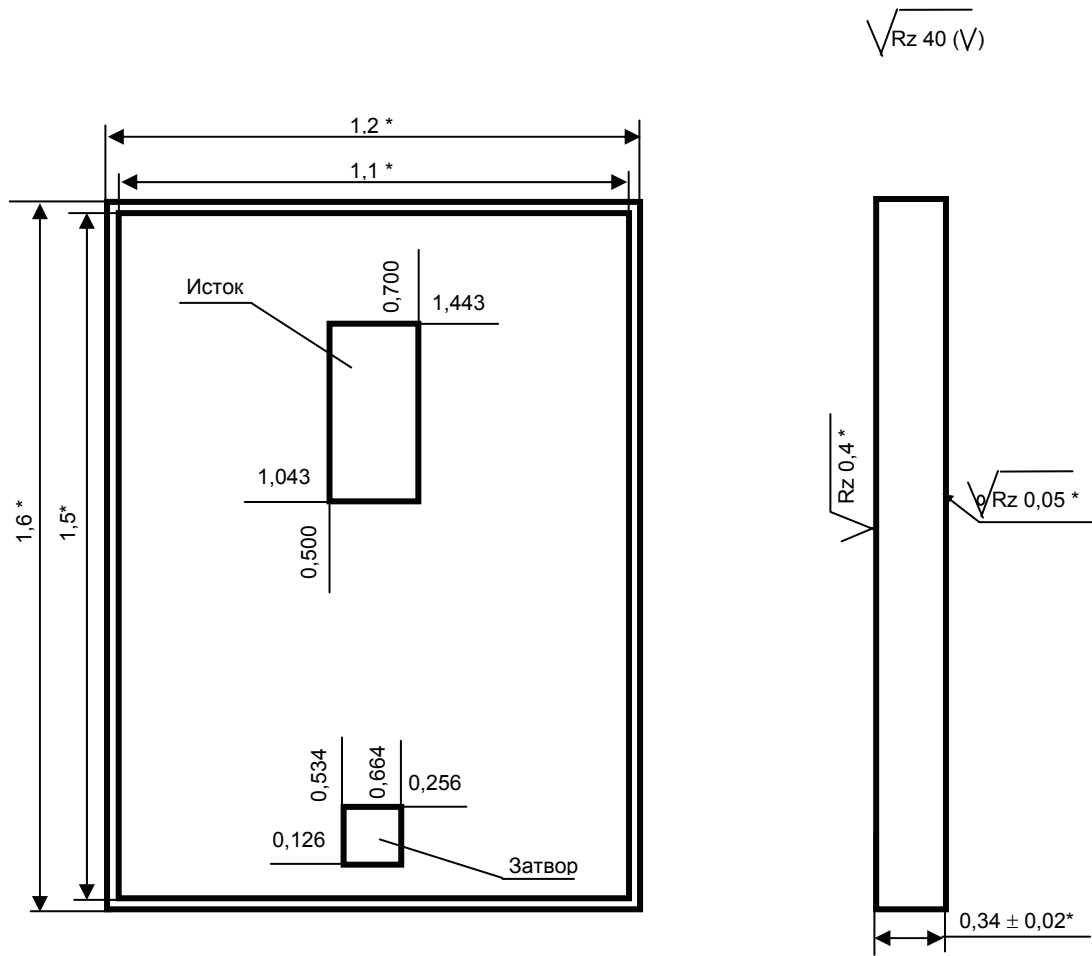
Габаритный чертеж кристалла 2П525А-5
